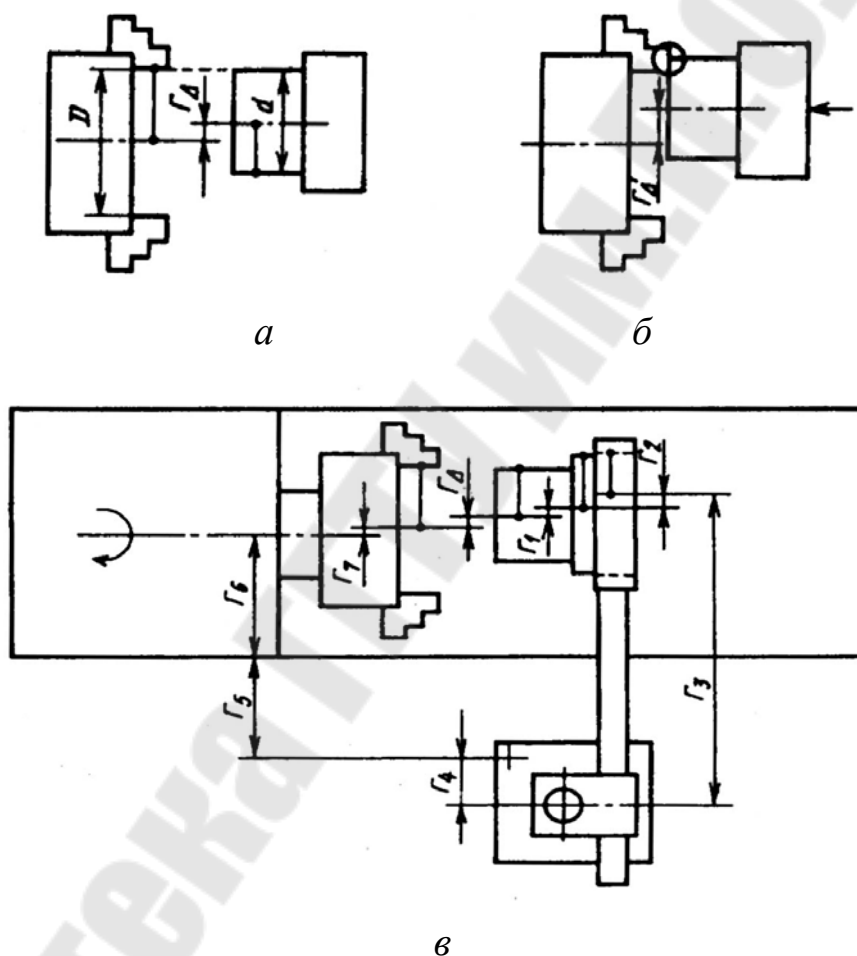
Схема размерных связей при автоматической загрузке станка
